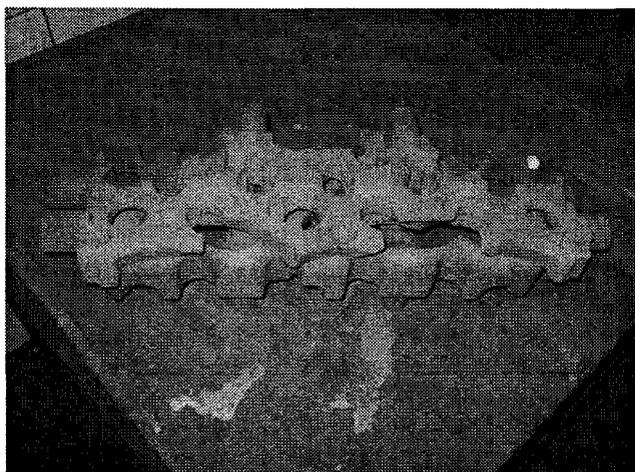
Изготовленный стержень для отливки «Головка цилиндра»
